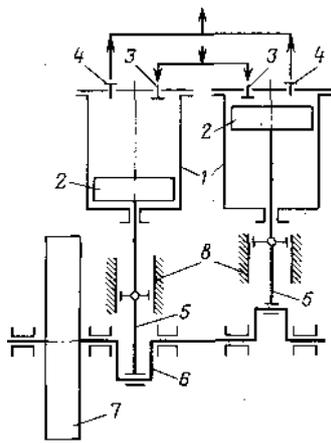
Двухцилиндровый компрессор простого действия: 1 – цилиндр, 2 – поршень, 3 – всасывающий клапан, 4 – нагнетательный клапан, 5 – шатун, 6 – кривошип, 7 – маховик, 8 – крейцкопф
